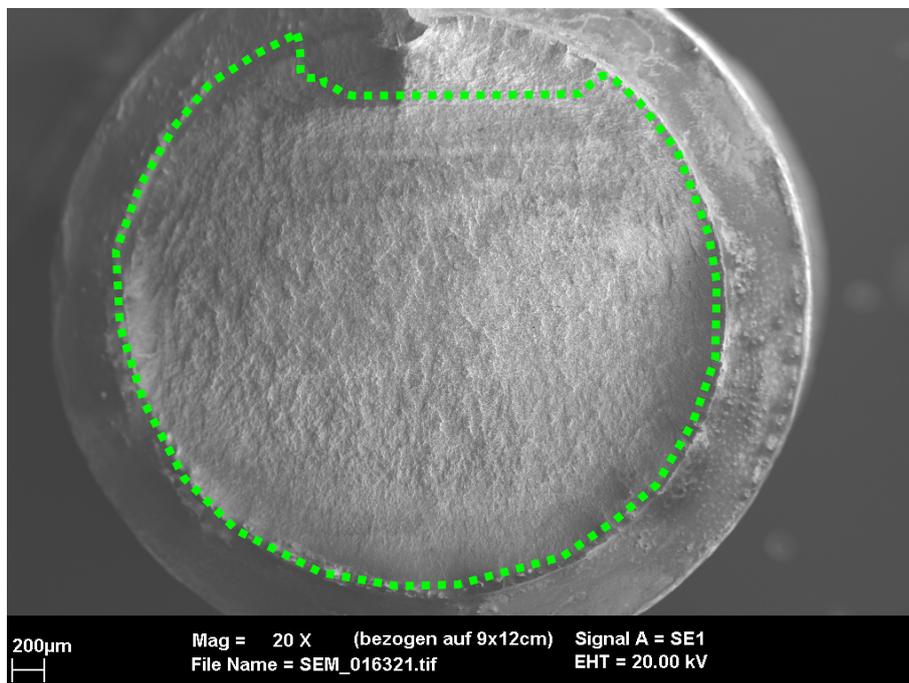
Bruchfläche der Schraube Nr. 1. Dauerbruchteil grün umrandet. Zahlreiche Stufen entlang des Gewindegrundes
